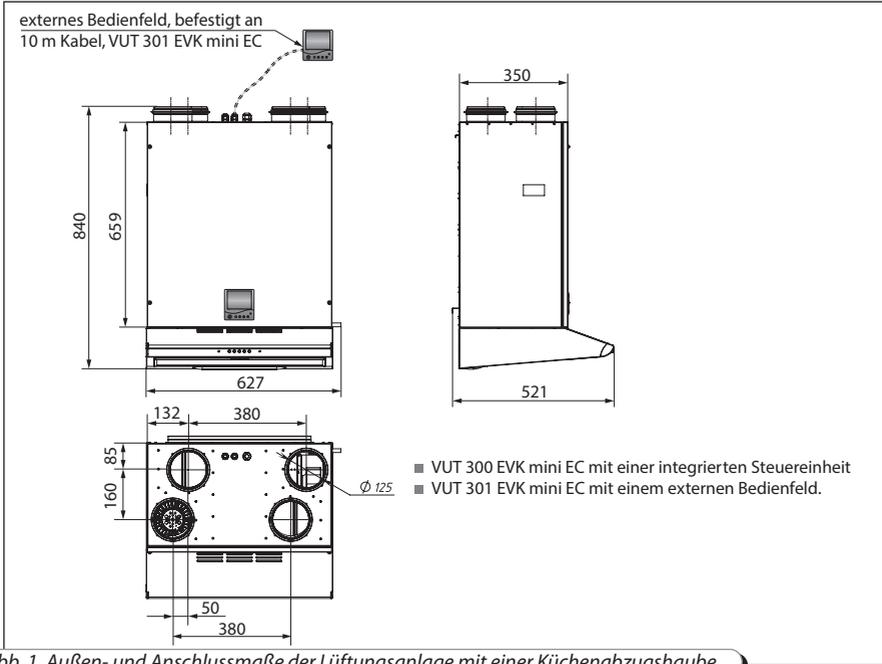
Außen- und Anschlussmaße der Lüftungsanlage mit einer Küchenabzugshaube
